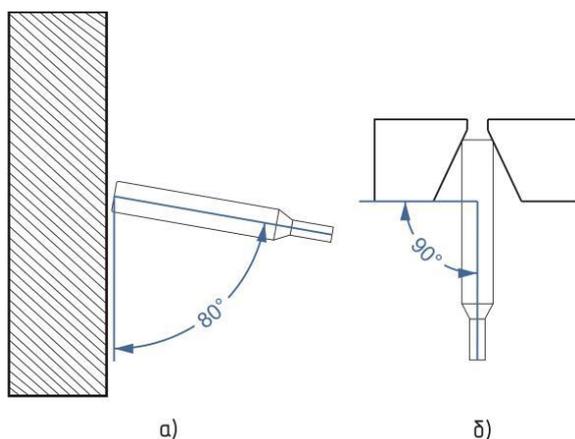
Углы наклона электрода при сварке в вертикальном положении сварного шва.
